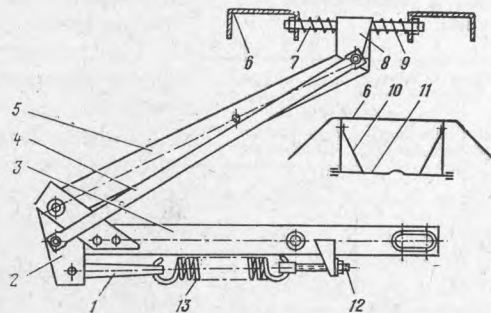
Конструкция каретки с увеличенным свободным ходом: 1 — серьга; 2 — кривошип; 3 — корпус; 4 — тяга уравнителя; 5 — рычаг; 6 — полз; 7 — шпилька; 8 — кронштейн; 9 — пружины; 10 — подкос; 11 — вал синхронизатора; 12 — болт синхронизатора; 13 — пружинное устройство
